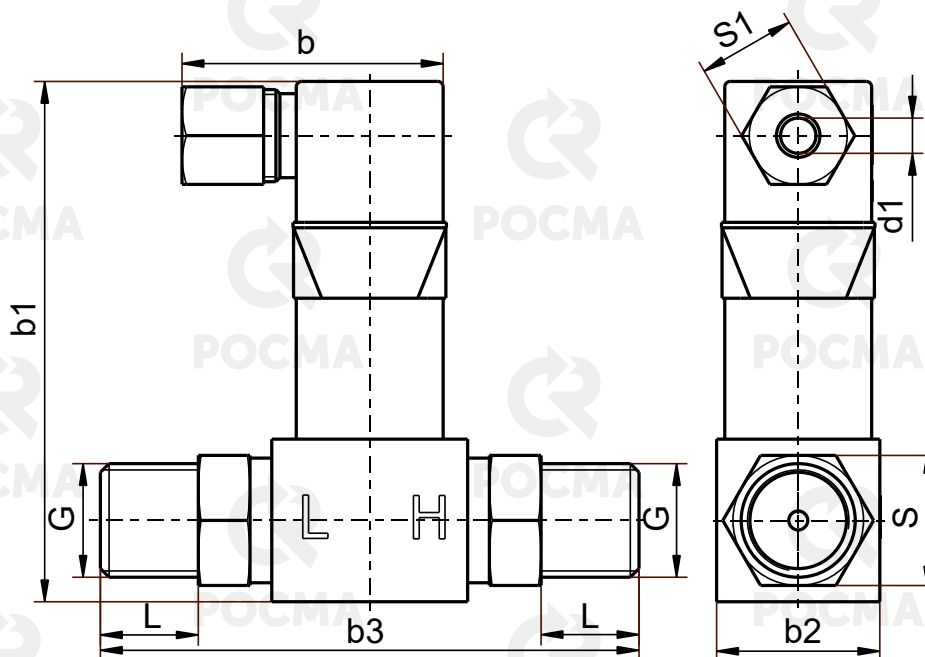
Габаритные и присоединительные размеры датчика давления измерительного РПД-Д.
